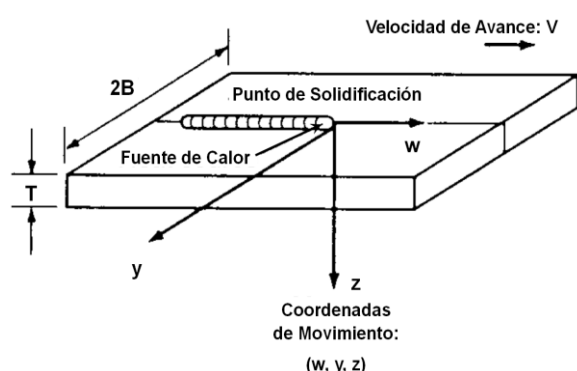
Esquema básico del modelo térmico de soldadura
